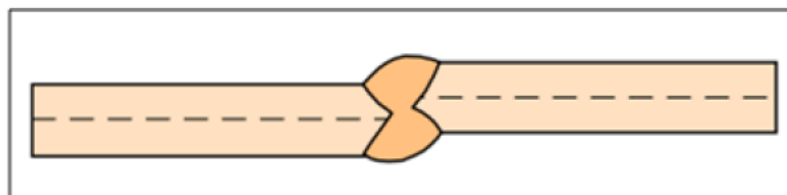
Esquema de junta soldada com desalinhamento
